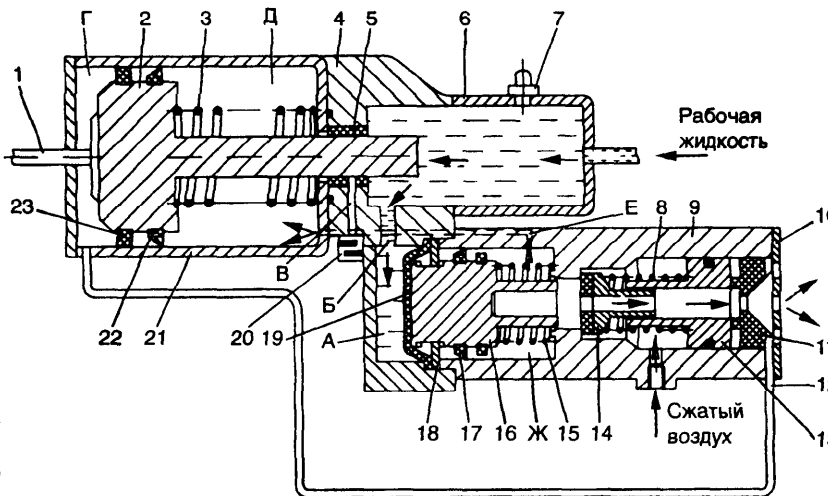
Конструктивная схема пневмогидроусилителя:
